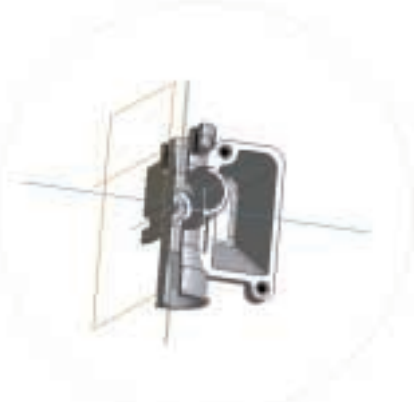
Корпус карбюратора K38, полученный модификацией корпуса K68
